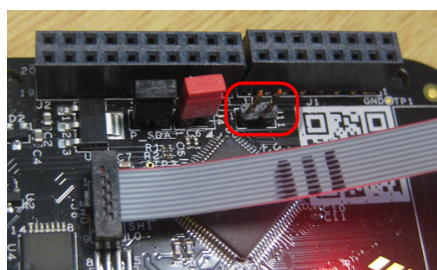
Passo 3: Soldadura de *header-pitch 2.54mm* no *solder jumper* SJ11;
